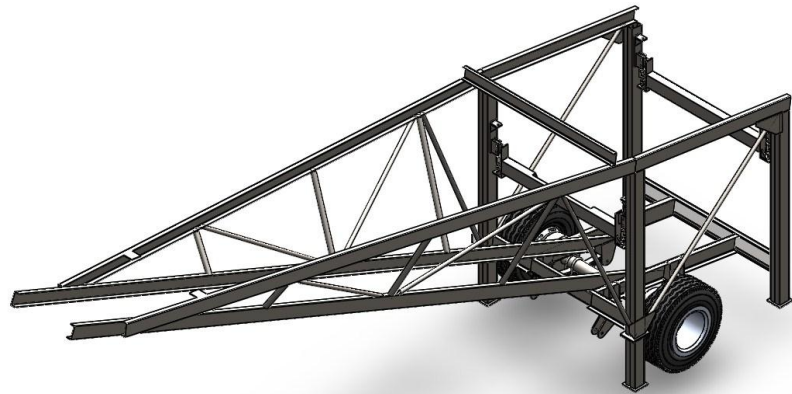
, Bastidor de planta de concreto - Vista isométrica
